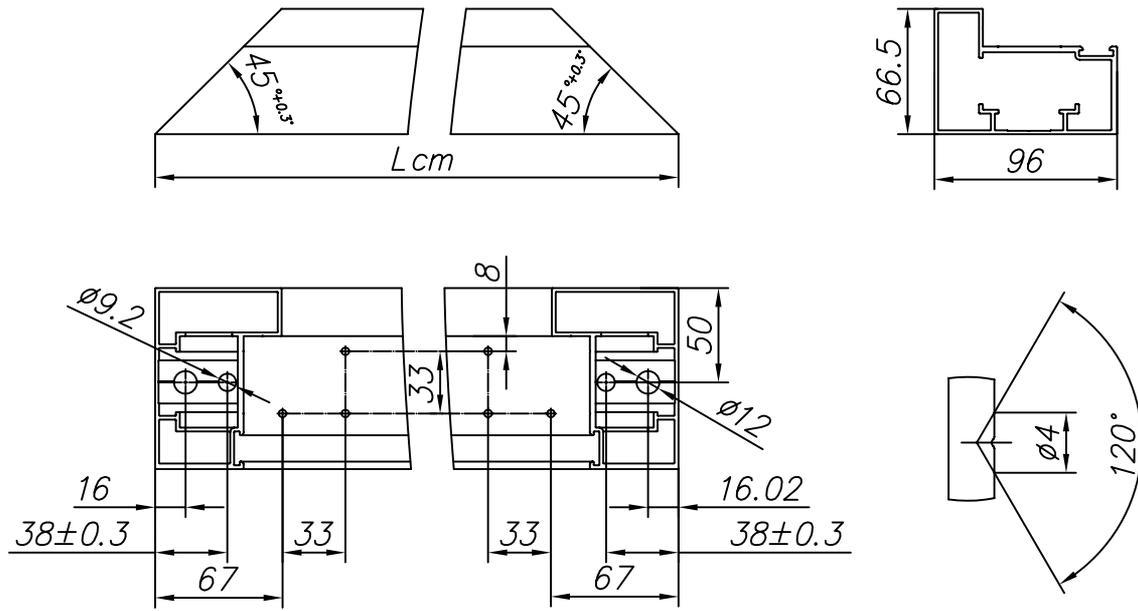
Изготовление стойки (профиль рамы FLGU.400.0102)
